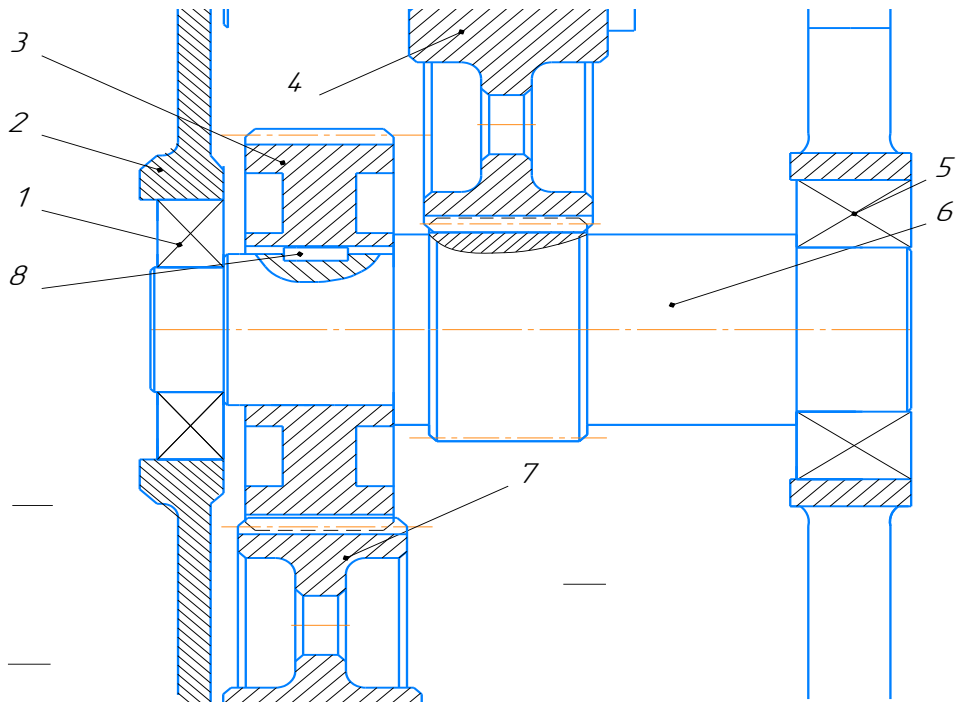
Ескіз вузла редуктора ТСН.02.102
